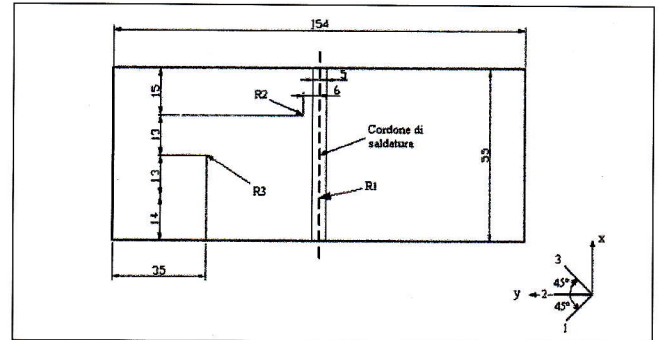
Disposizione delle rosette sul pezzo estruso.
